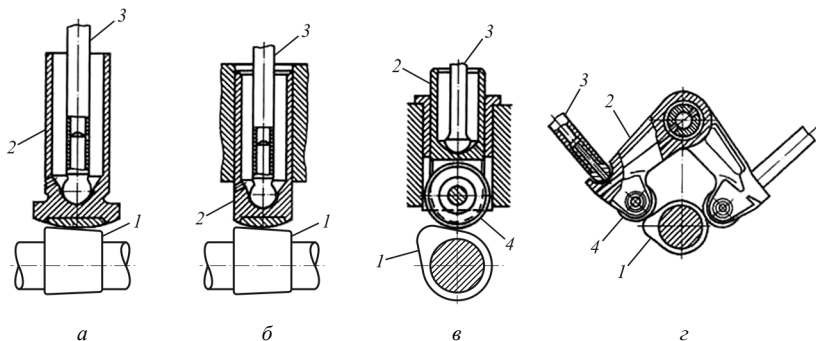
Типы толкателей: а – грибовидный; б – цилиндрический; в – цилиндрический роликовый; г – рычажный роликовый; 1 – кулачок распределительного вала; 2 – толкатель; 3 – штанга; 4 – ролик
